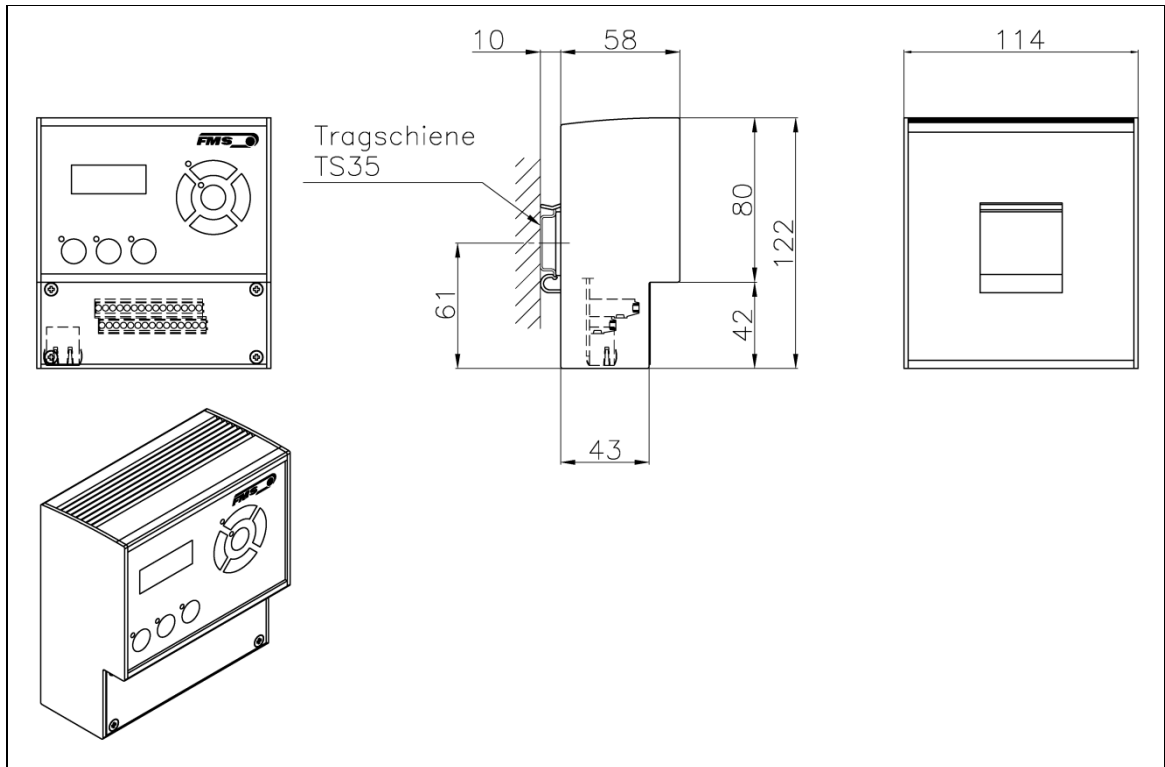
CMGZ309.R Gehäuse für DIN-Schienenmontage
